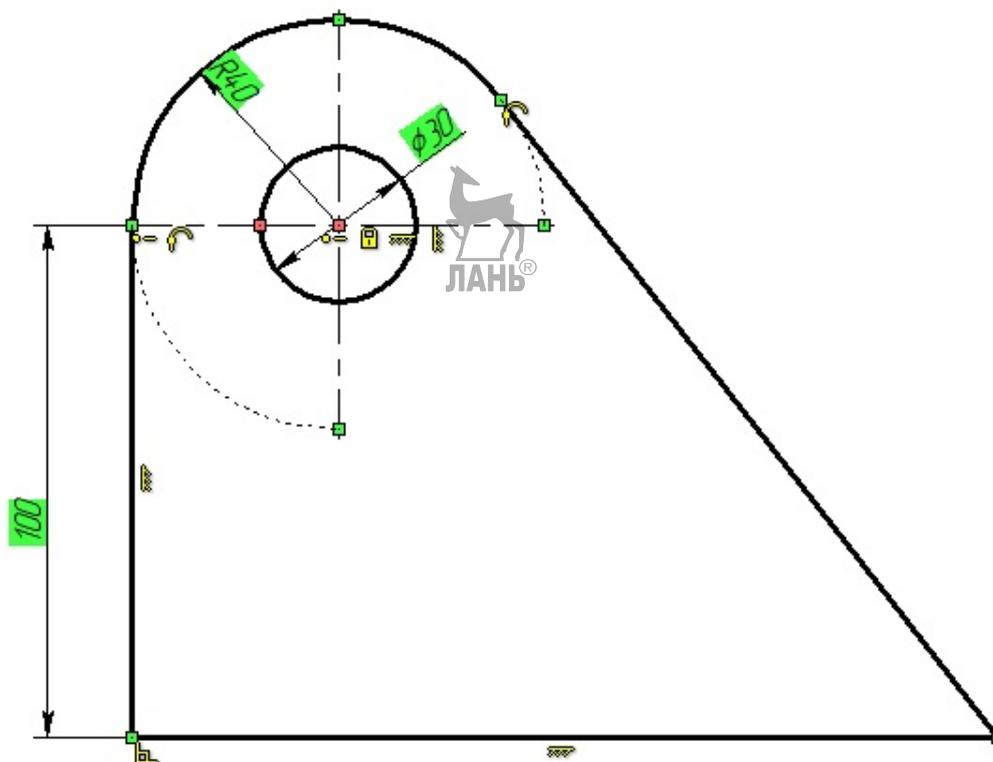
Параметрический чертеж уха с другими заданными параметрами размеров (цвет всех линий черный, фон управляющих размеров зеленый)
